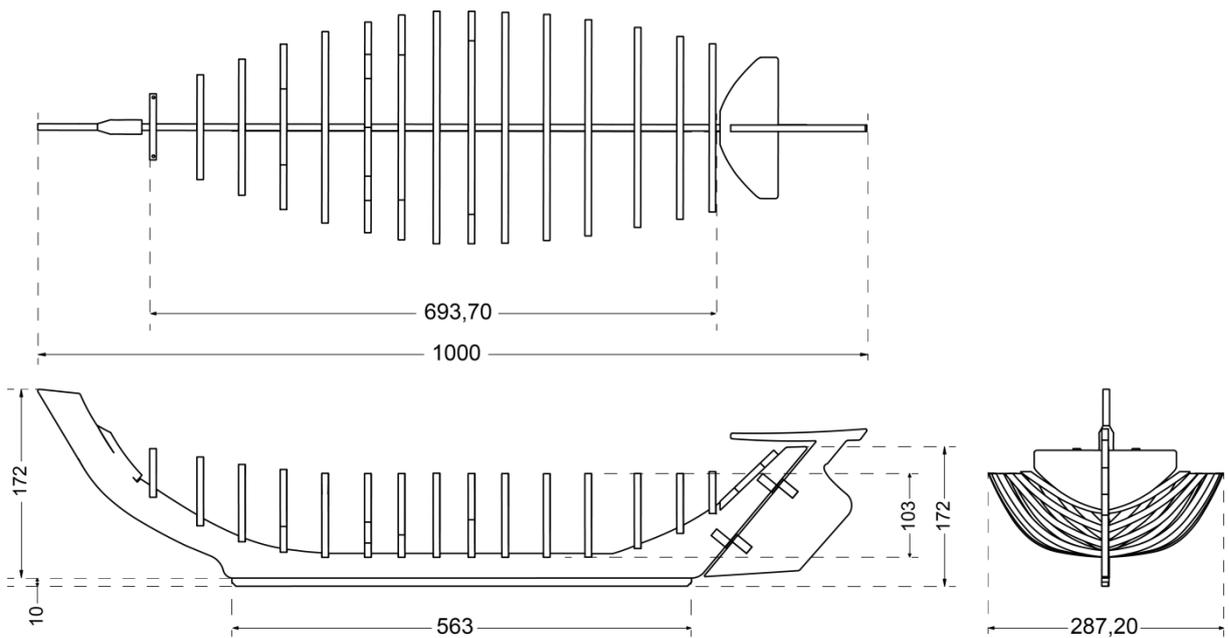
dimensões gerais da estrutura da canoa do saveiro.
